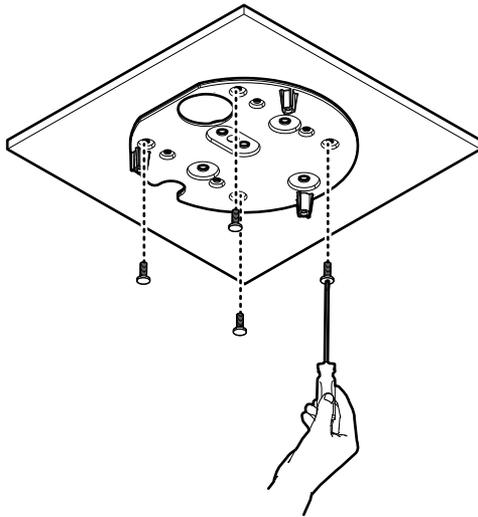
Закрепления монтажной пластины: накладное крепление с защитой от внешних воздействий/вандализма
